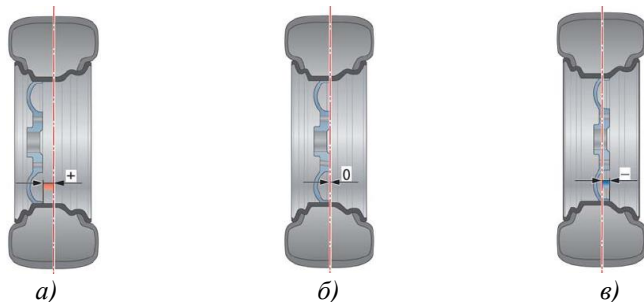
Вылет колёсного диска: а) положительный, б) нулевой, в) отрицательный
